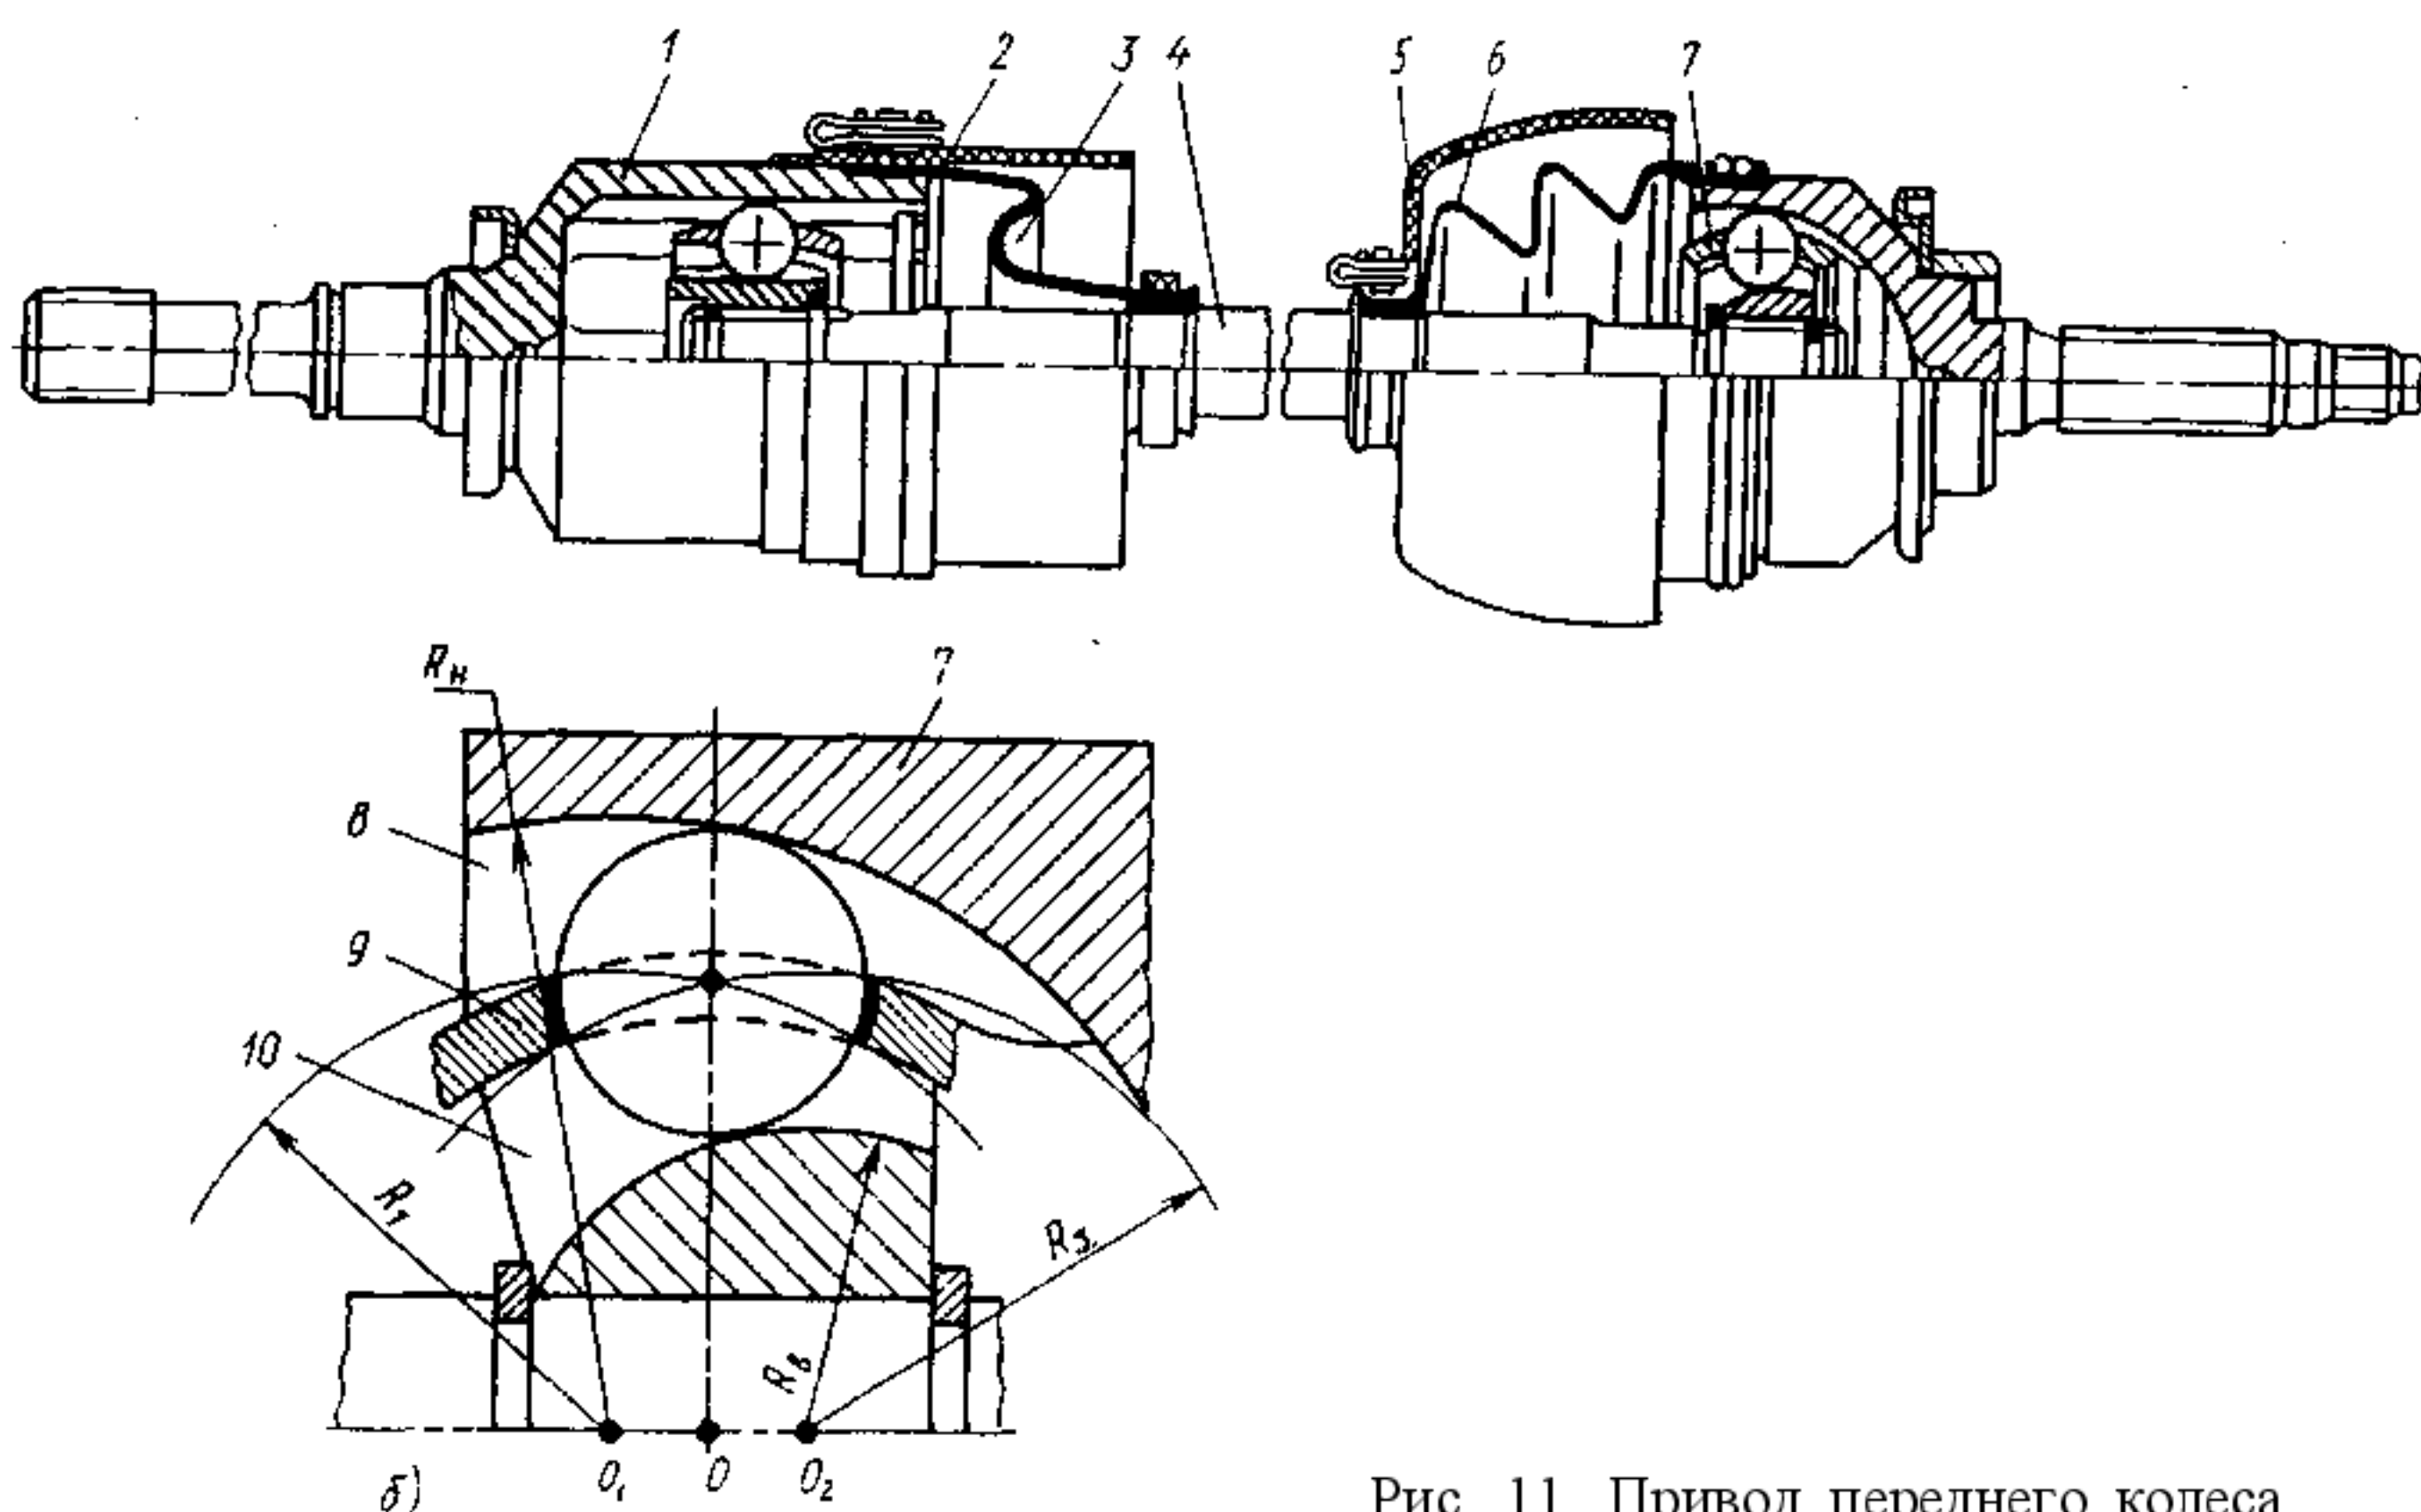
Привод переднего колеса автомобиля ВАЗ-2121 «Нива»: а - конструкция; б - схема наружного шарнира
